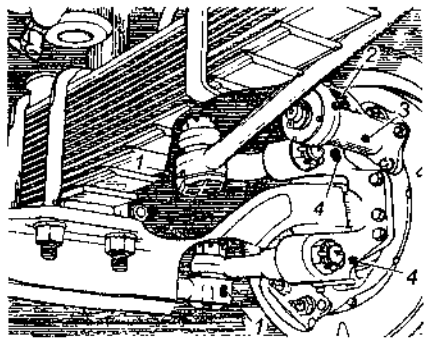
Расположение на автомобиле пресс-масленок для смазывания: 1 — шарниров рулевых тяг; 2 — регулировочного тормозного рычага; 3 — разжимного кулака; 4 — втулок шкворней
